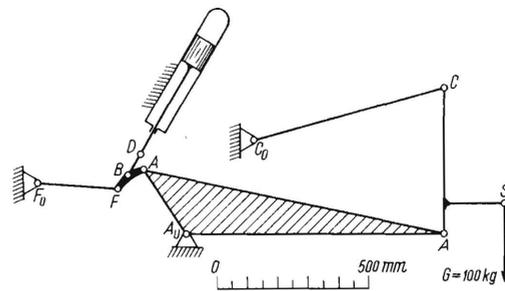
Einbau des Getriebes mit festem Zylinder nach Bild 26 in das Gesamtgetriebe.
